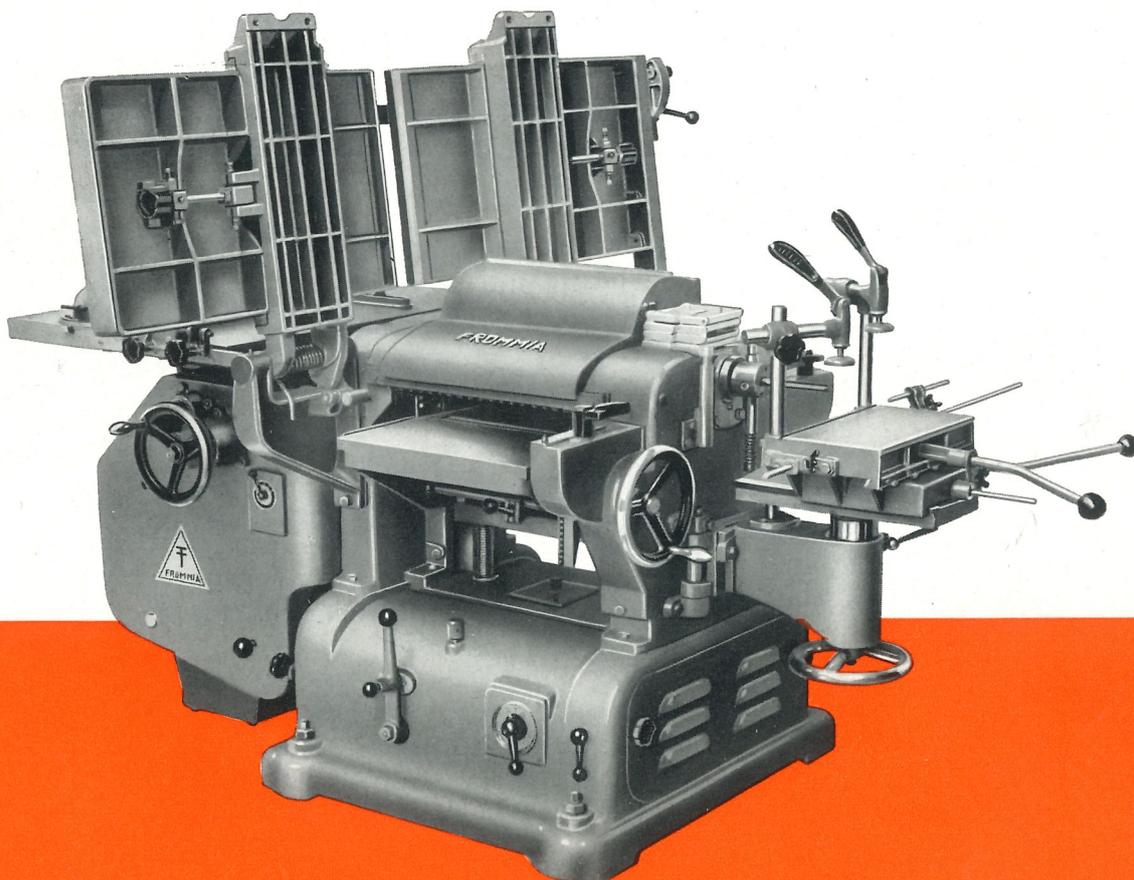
Nr. 261 UB. 5-fach kombinierte Abrichte, Dicke, Fräse, Kreissäge und Bohrmaschine mit hochgeklappten Abrichttischen und aufgesetzter Spänehaube
